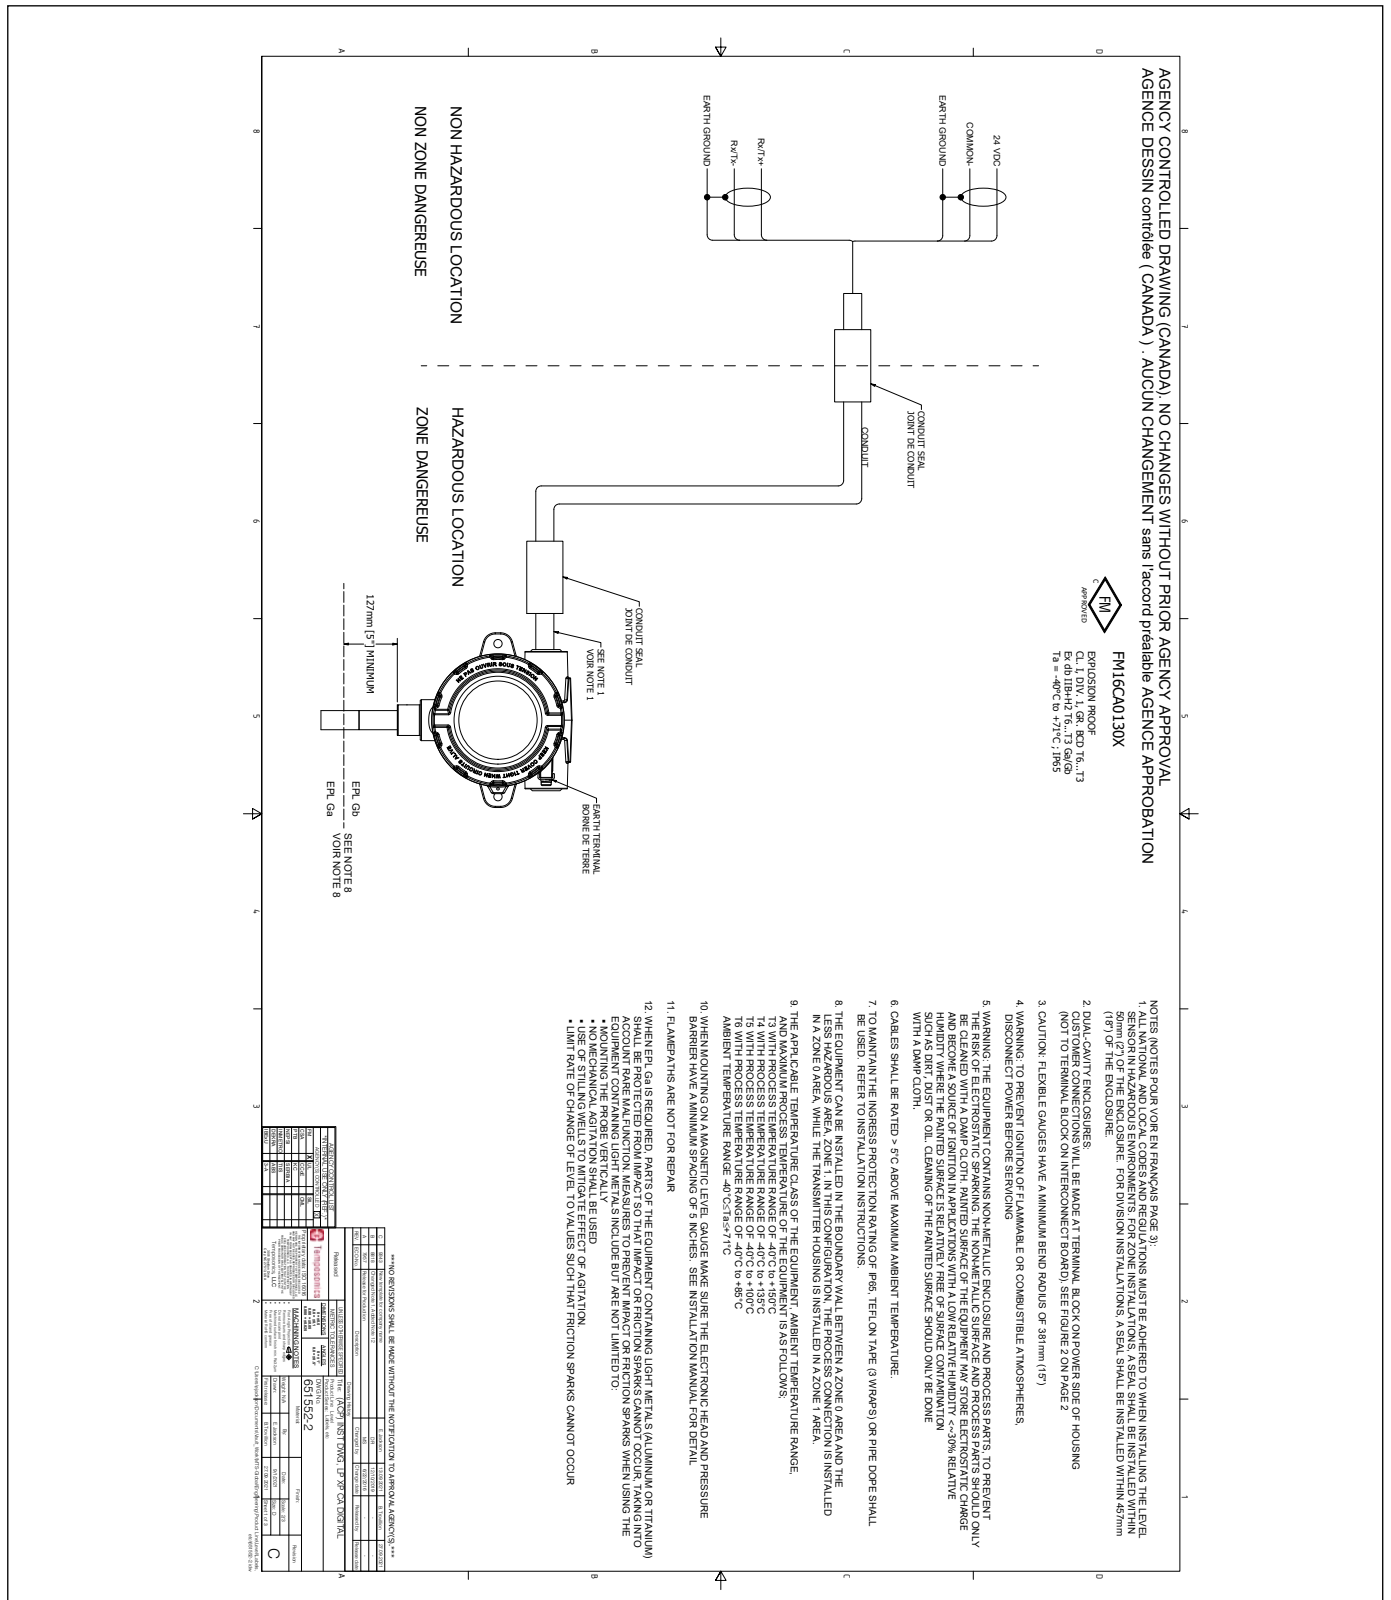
Explosionsgeschützt, FMC-Montagezeichnung, Modbus und DDA, Seite 1
